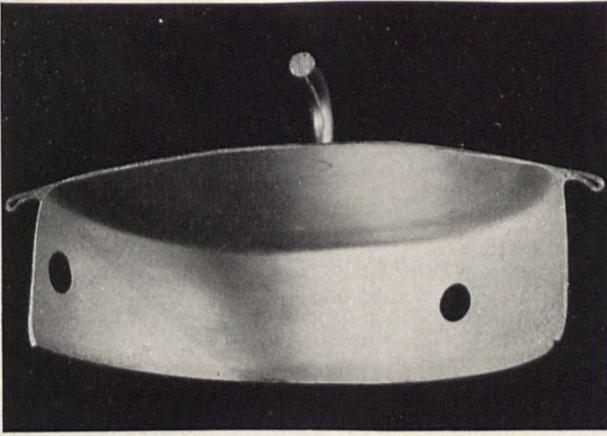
Auch dieser Milchkannendeckel ist richtig ausgeführt. Die Randfalte wurde zugeschweißt.
